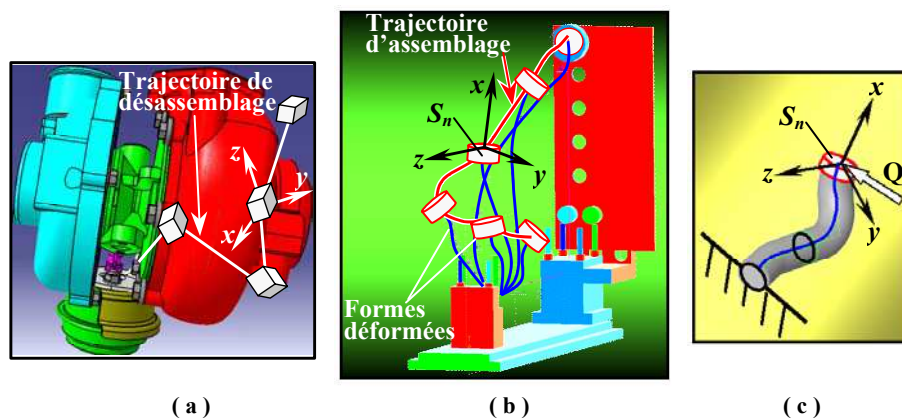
Exemples de manipulation de pièces virtuelles :
